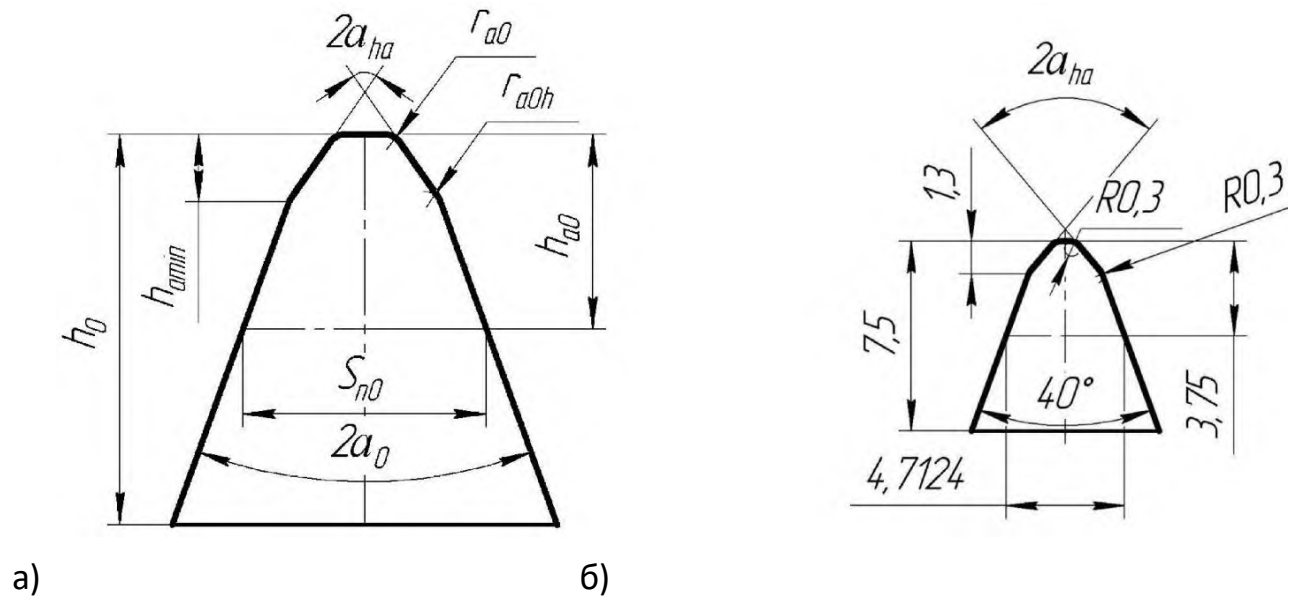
а) профіль зуба фрези, що дозволяє виключити особливу точку на поверхні зубчастого колеса, що обробляється. б) розрахунковий профіль ВПІ конволютної черв'ячної фрези призначеної для формоутворення без підрізання зубчастого колеса: $m=3$, $Z_k=10$, $x=+0.3485$, $b_k = 0^\circ$, діаметр вершин зубів колеса $d_{a1}=38.1$, діаметр западин $d_{f1}= 24.7$, фреза конволютна $d_a=80$, $r_{a0}=0.05$
